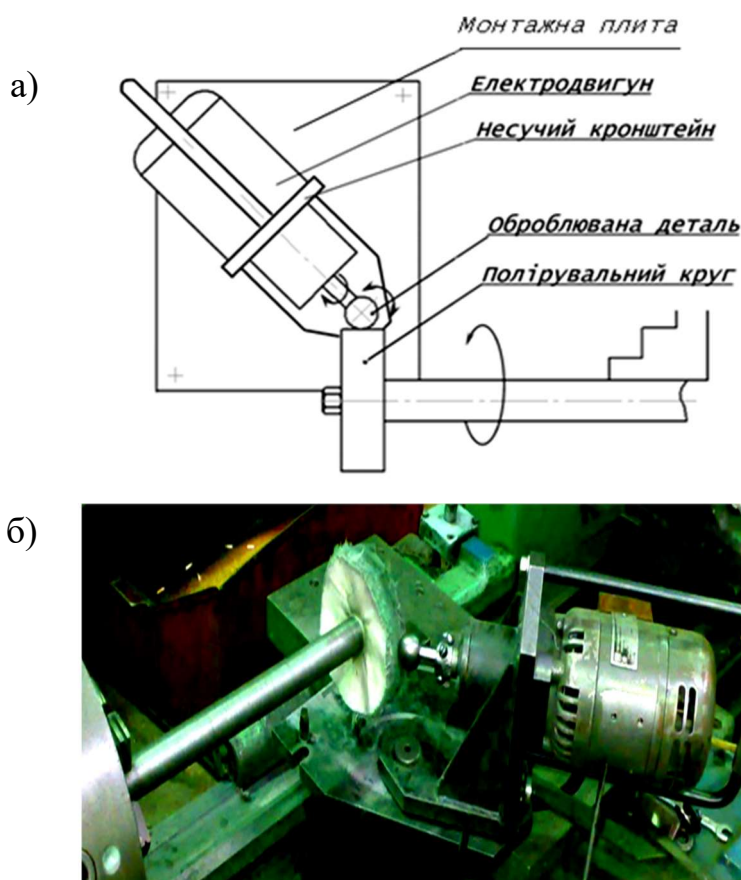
Полірування сферичної заготовки: а) схема пристрою та основні рухи; б) фото пристрою
